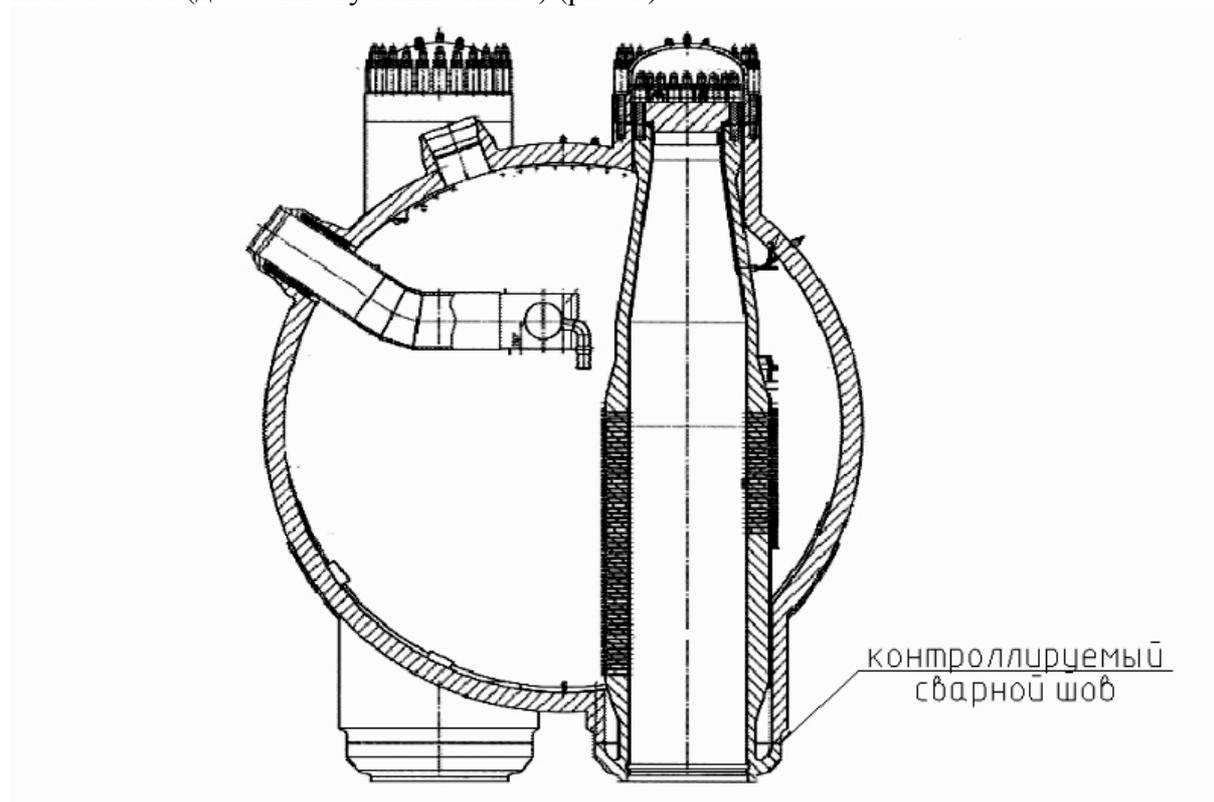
Парогенератор ПГВ-1000М. Расположения сварного шва
